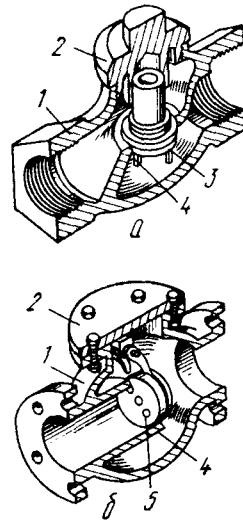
Обратный клапан: а — подъемный; б — поворотный
